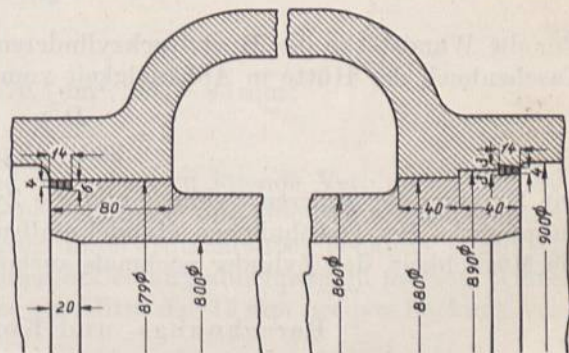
Befestigung und Abdichtung des Laufzylinders im Mantel, Abb. 1745.
